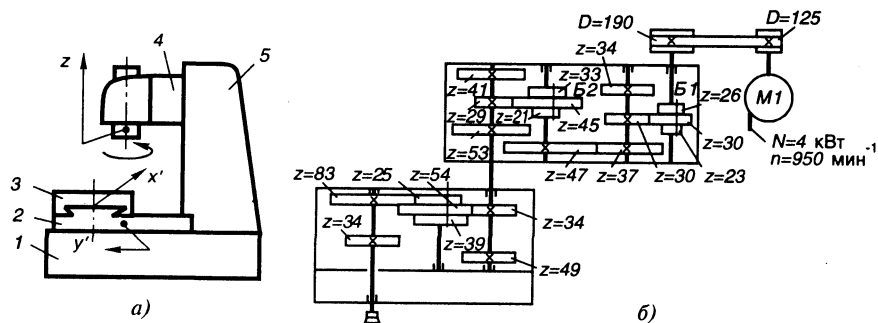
Общий вид (а) и кинематическая схема привода главного движения станка 6520Ф3(б)
